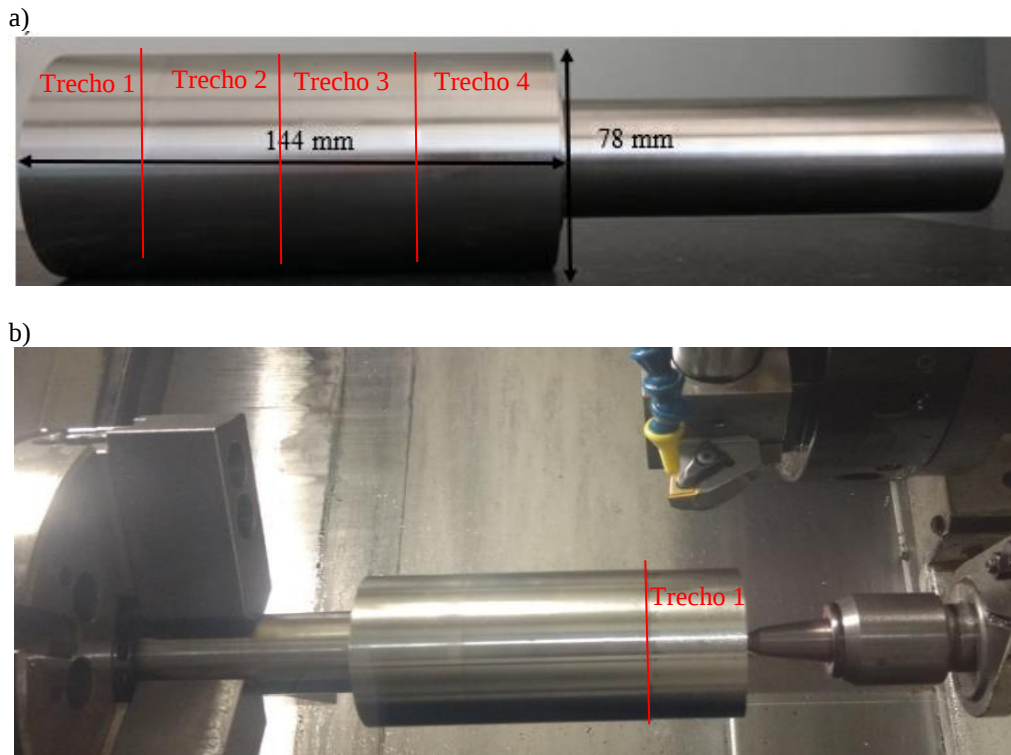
a) Dimensões iniciais do corpo de prova Inconel 718, apresentando os trechos usinados. b) Corpo de prova fixado na placa de três castanhas do torno. Visualização do primeiro trecho usinado. (Adaptado de Pinheiro 2018).
